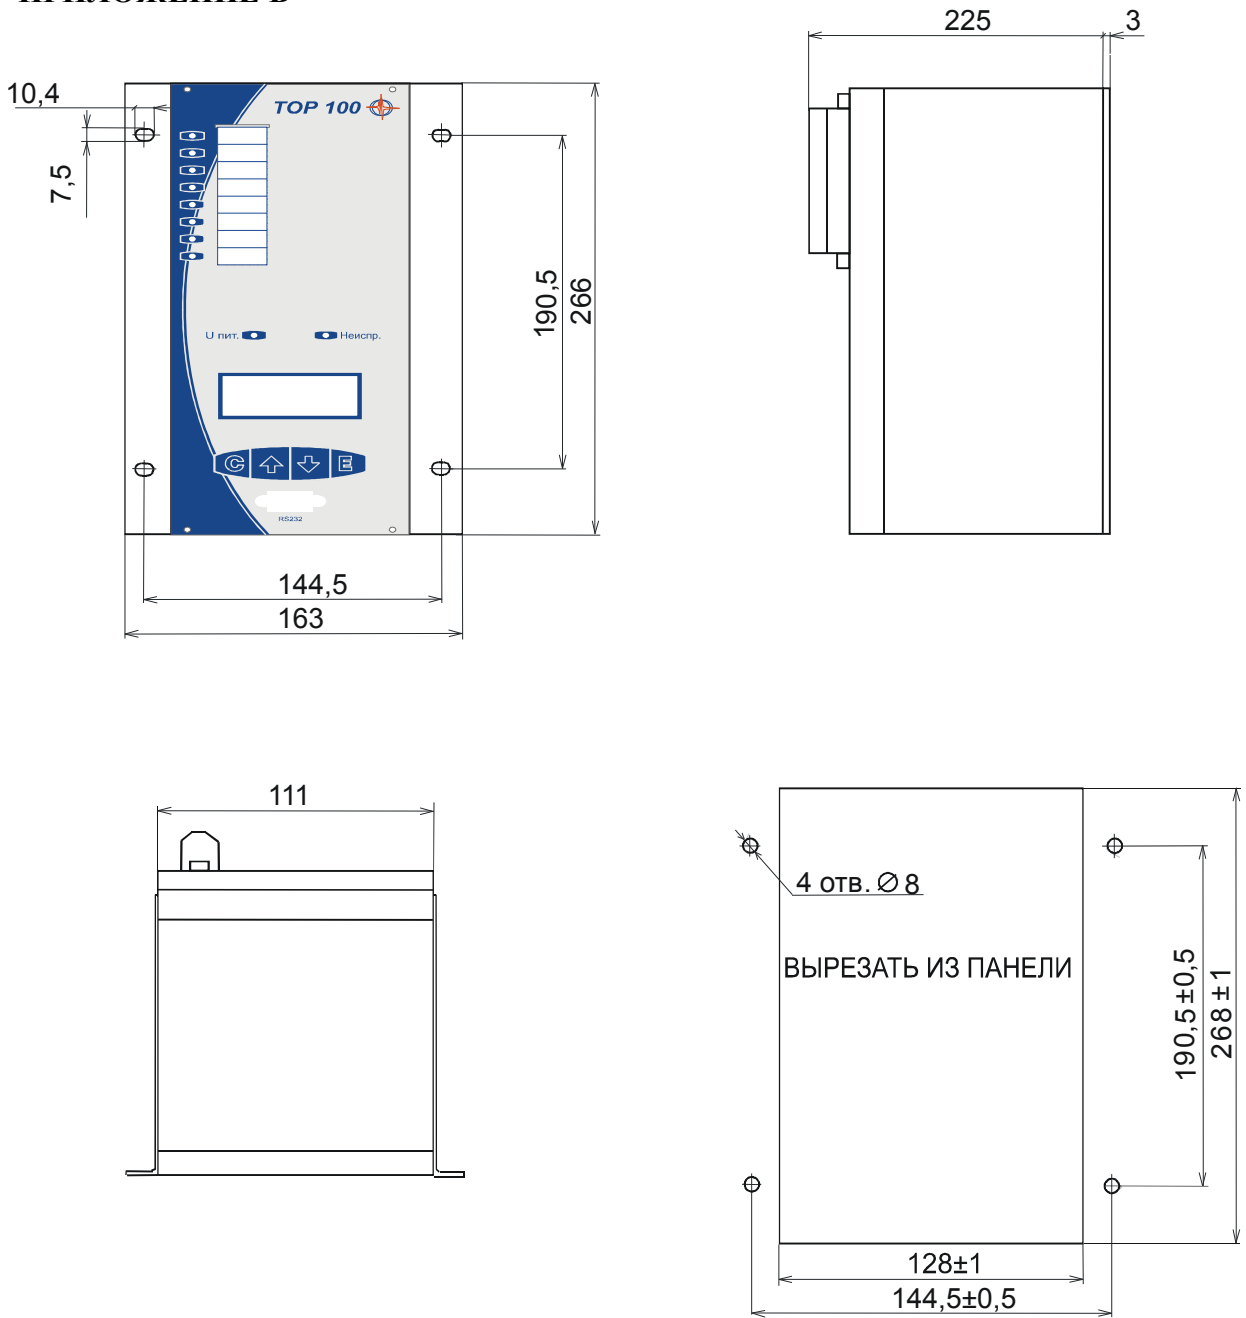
Габаритные и установочные размеры TOP 100
